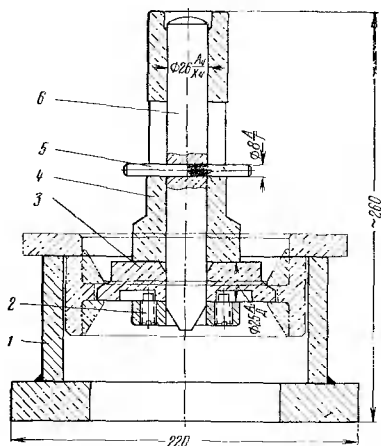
Приспособление для выпрессовки наружных колец подшипников из картера подшипников вала ведущей шестерни:
